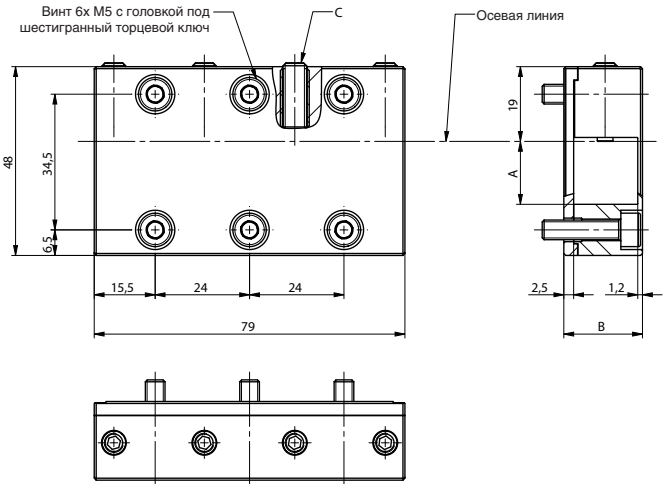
Держатель инструмента для резца токарного станка с аксиально установленным динамометром, тип 9119AE...
